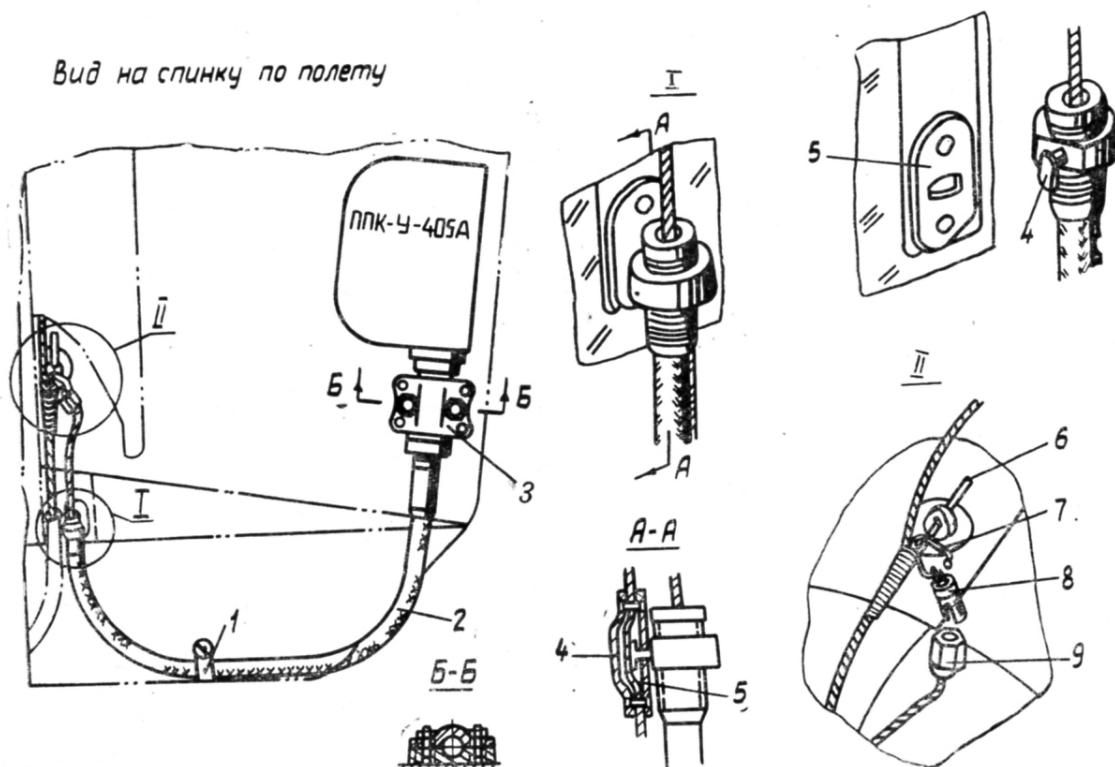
Установка прибора ППК-У-405А на спинку кресла:
